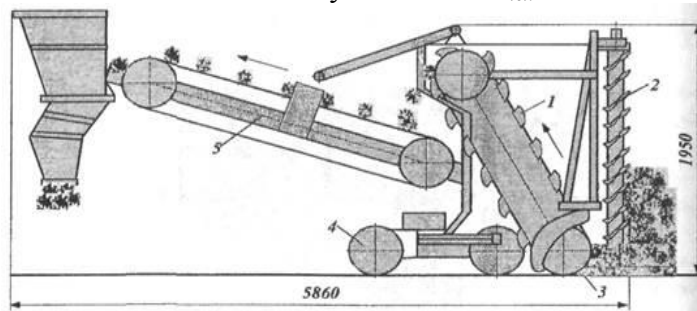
Схема МВС: 1—ковшовой элеватор; 2—шнековый вертикальный рушитель; 3—питатель; 4—гусеничный двигатель; 5—отвальный конвейер
